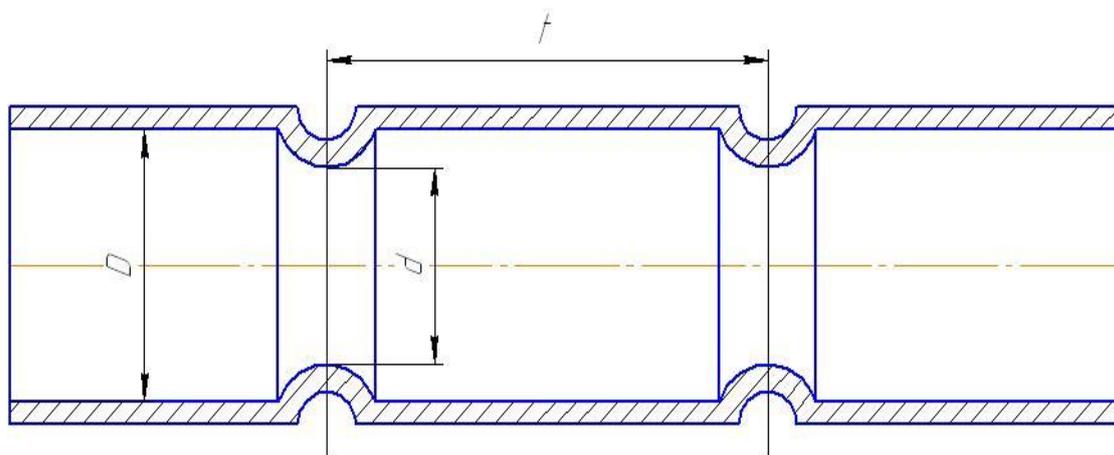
Продольный разрез трубы с зигами на наружной стороне и плавно очерченными выступами внутри
